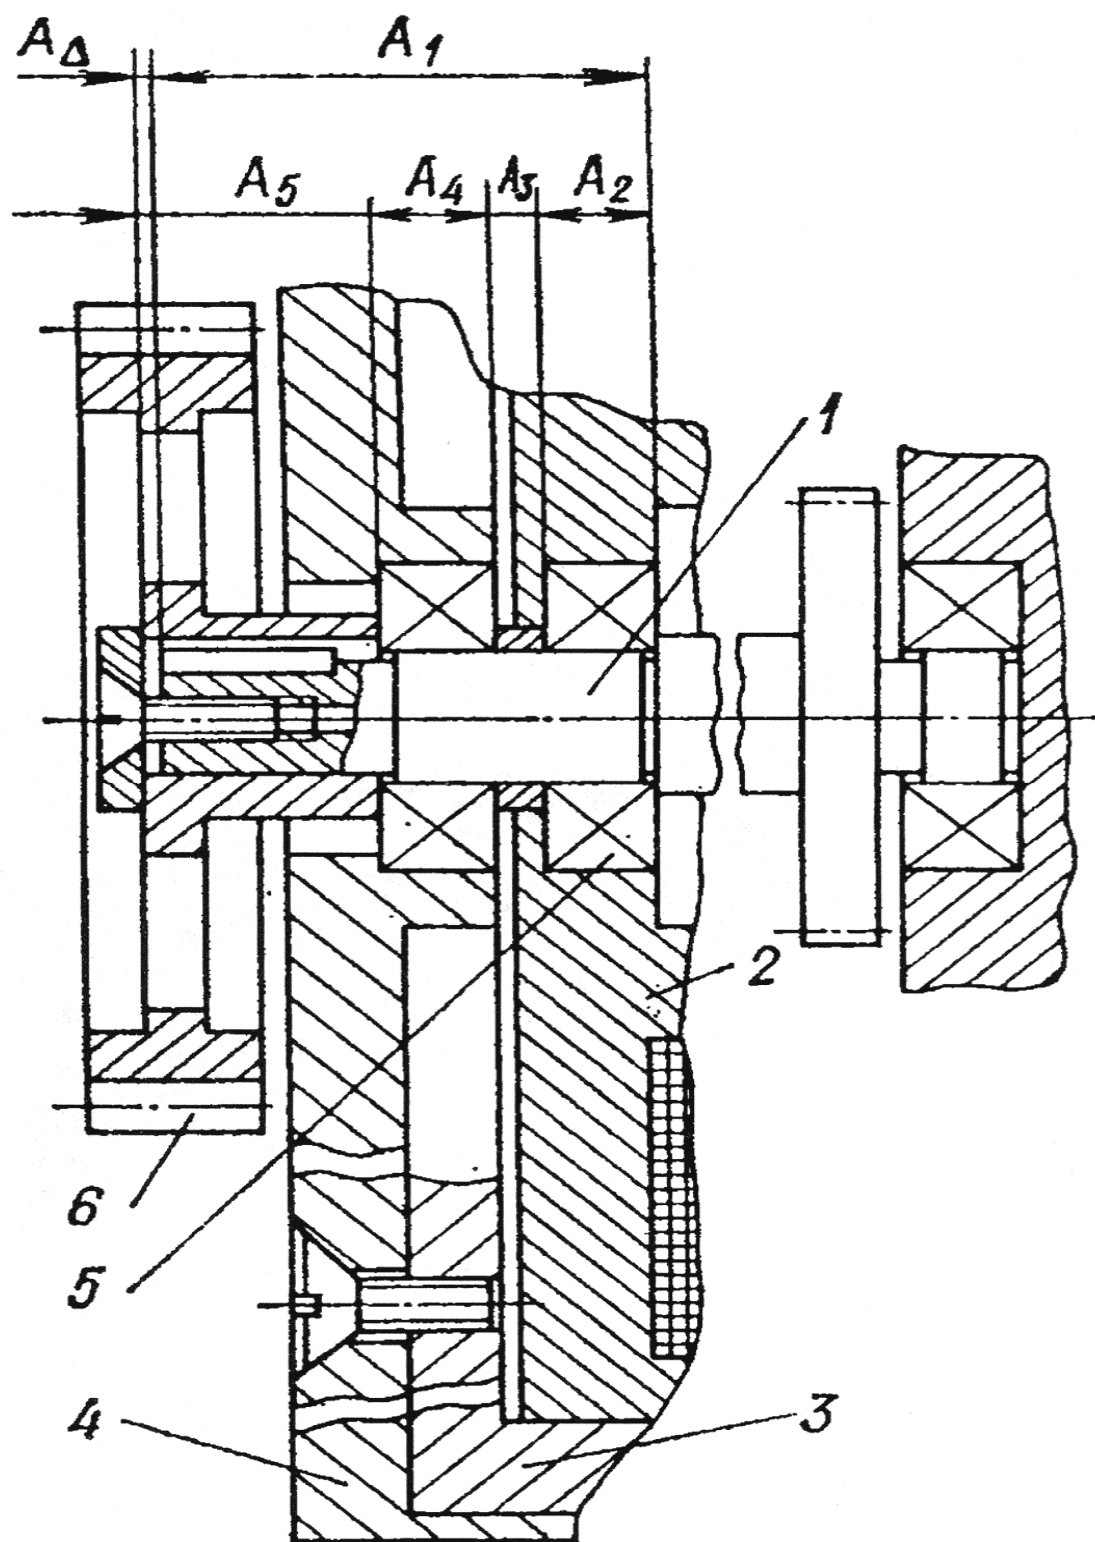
Узел подшипникового соединения: 1 – вал; 2 – вкладыш; 3- корпус;
